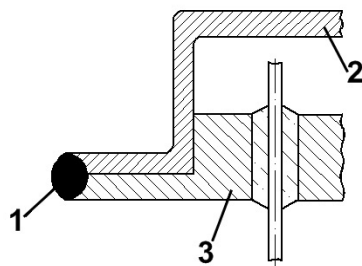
Конструкция сварного соединения при сварке плавлением
